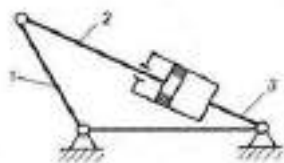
Кулисный механизм: 1 — кривошип; 2 — шатун; 3 — поршень
